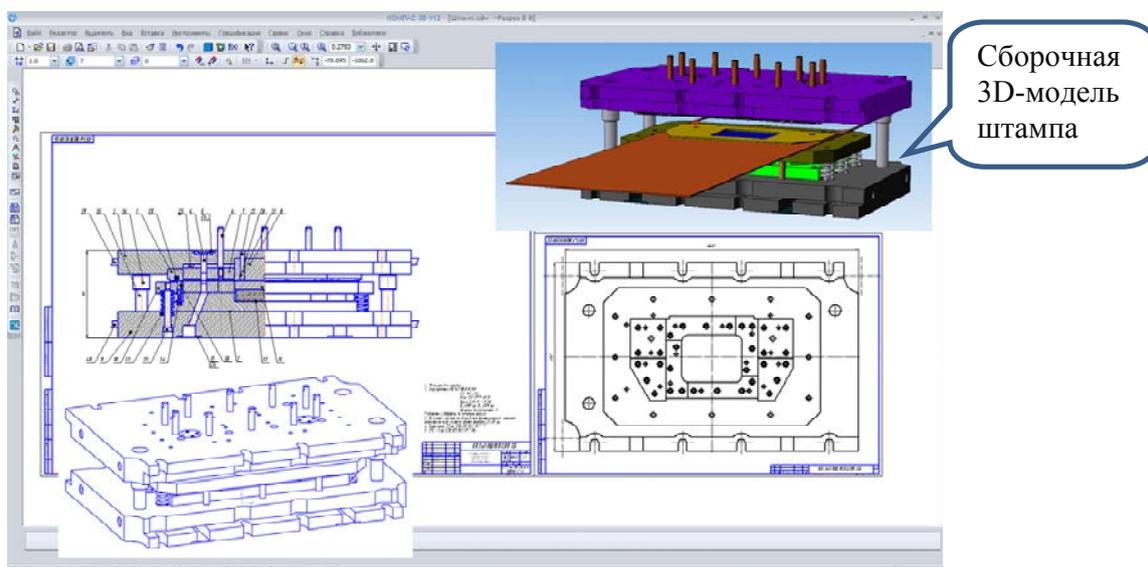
Ассоциативный сборочный чертеж штампа, созданный по его 3D-модели
